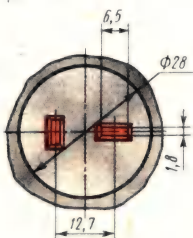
Крышка розеточной части электрического соединителя 42 В, 10 А для приборов класса защиты III
